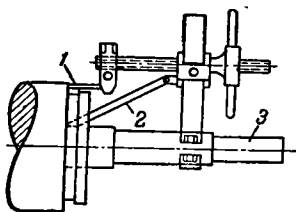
Приспособление для вытаскивания роторных стержней.
